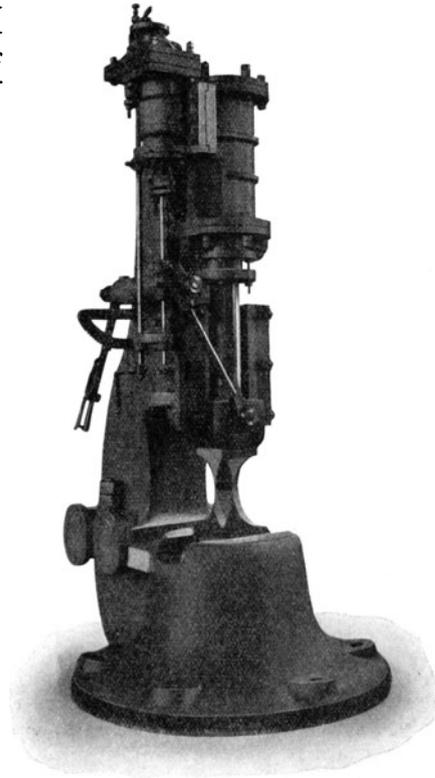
Dampf-Schnellhammer mit 200 kg Fallgewicht, 400 mm Hub und 225 mm Zylinderdurchmesser, gebaut von der Eschweiler-Ratinger-Maschinenbau - A. - G.¹⁾
